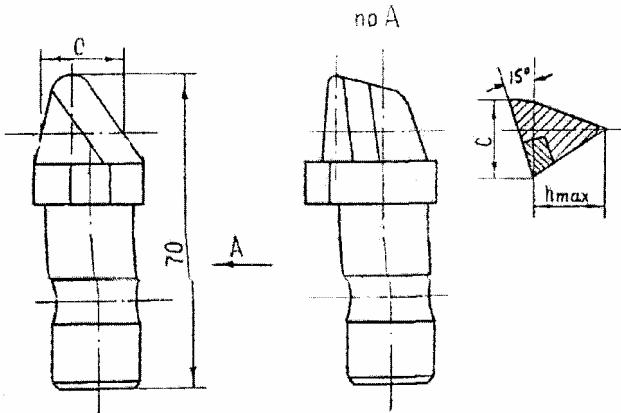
Резец КузГТУ с цилиндрической державкой и частичной армировкой передней грани твёрдым сплавом
